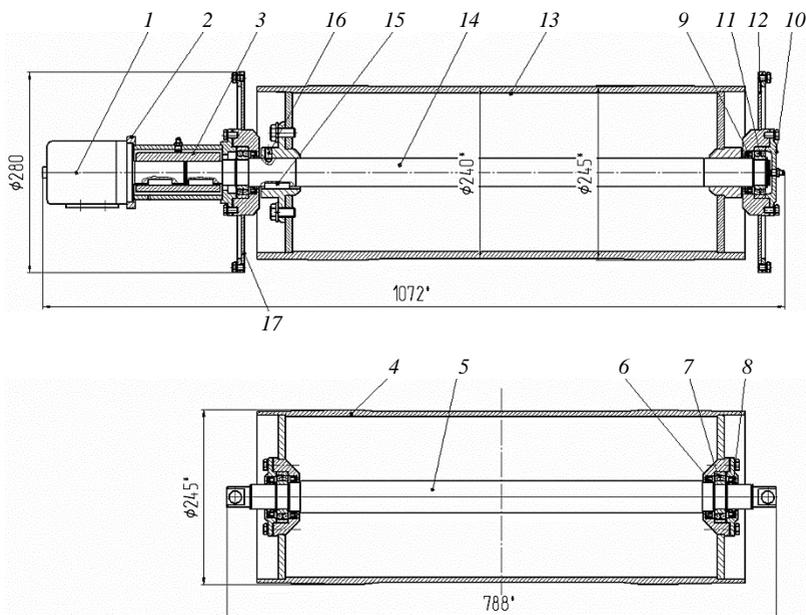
Ведущий и натяжной барабаны транспортера: 1 – гидромотор; 2 – стакан; 3 – муфта втулочная; 4, 13 – барабаны; 5 – ось; 6, 8, 9 – манжеты; 7, 11 – подшипники; 10 – крышка; 12, 17 – кронштейны; 14 – вал ведущий; 15 – шпонка; 16 – винт стопорный
